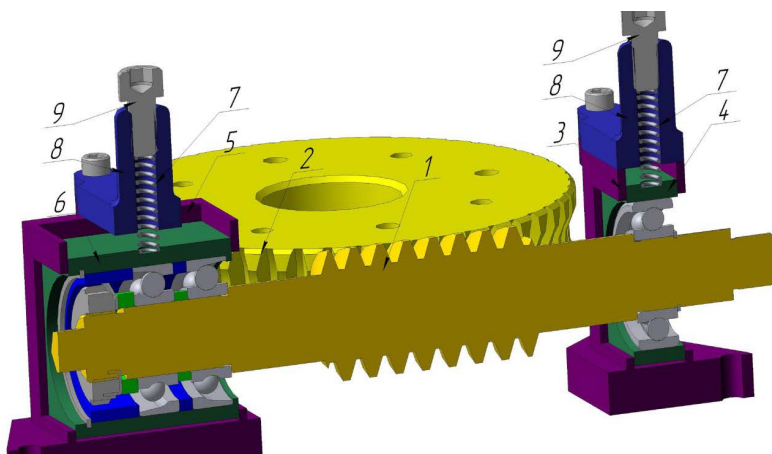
Скользящие опоры червяка: 1 – червяк; 2 – червячное колесо; 3 и 5 – корпус скользящей опоры; 4 и 6 – подшипники в скользящих опорах червяка; 7 и 8 – корпус пружины; 9 – винт, регулирующий натяг пружины
